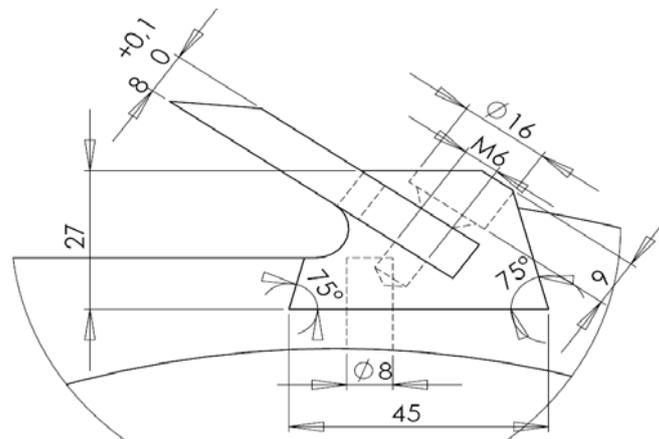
Vue de dessin de l'assemblage {corps d'outil+insert 55° +couteau},
